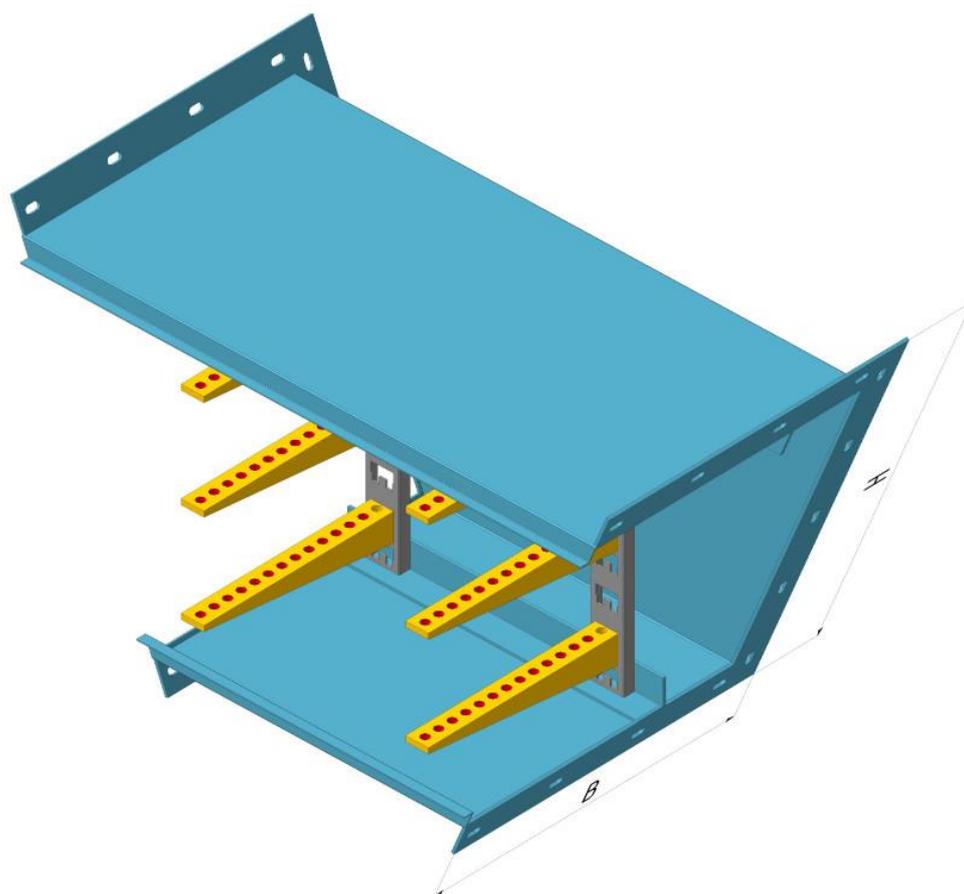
Короб кабельный блочный угловой с поворотом вниз типа ККБ-УН. Общий вид
